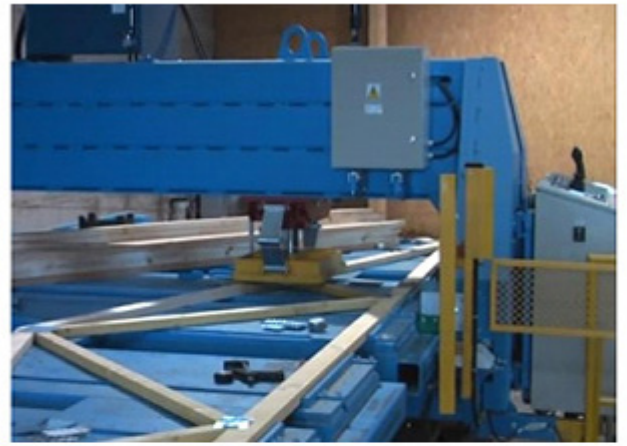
Изготовление и монтаж деревянных конструкций с МЗП
